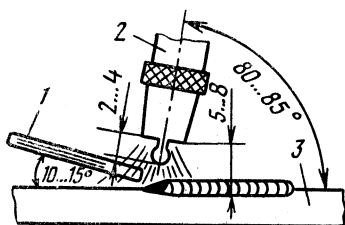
Взаимное расположение мундштука и присадочного материала при аргоно-дуговой сварке:
